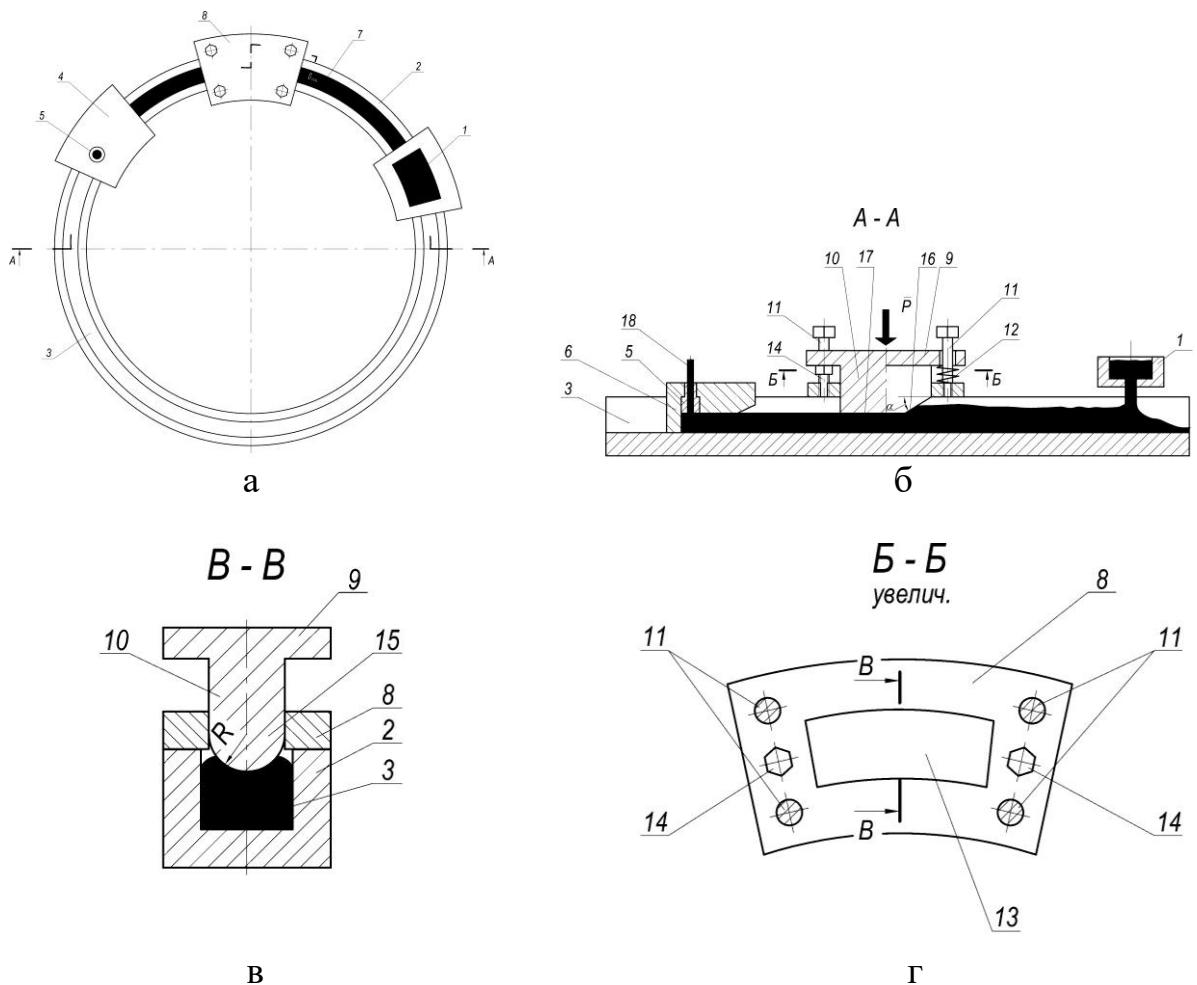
Схема установки для непрерывного литья и прессования металла с горизонтальным кристаллизатором [95]:
